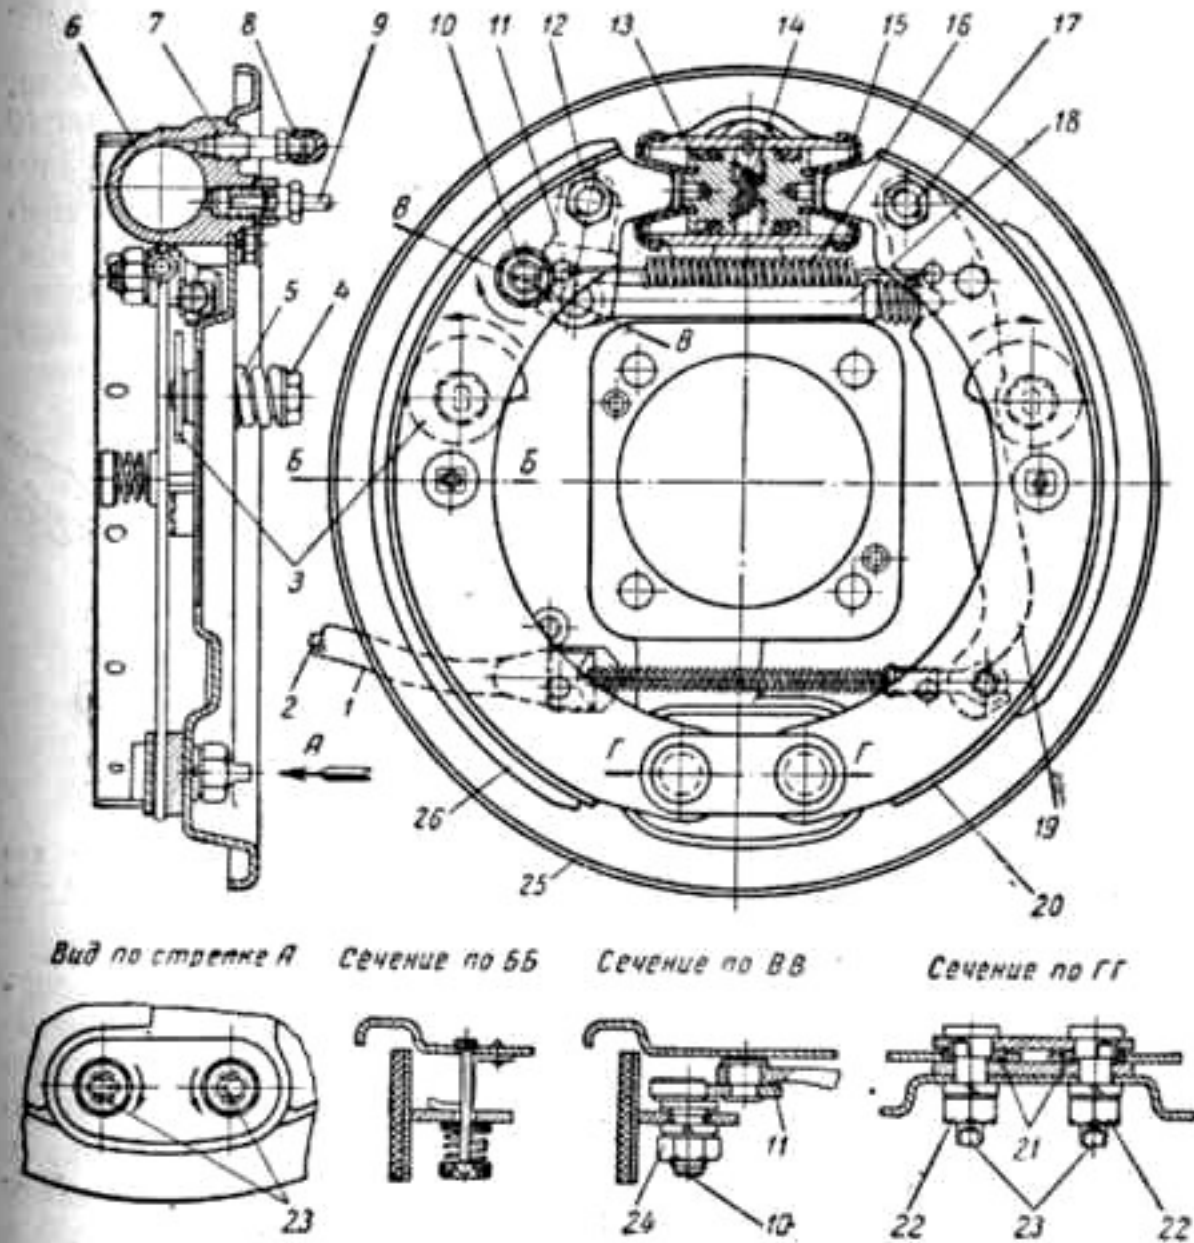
Колесный цилиндр тормоза заднего колеса:
